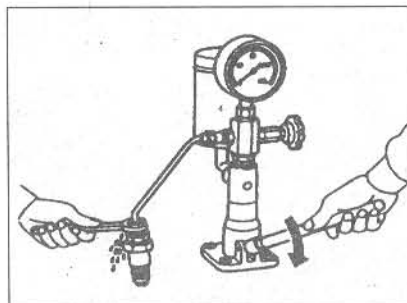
Проверка давления начала впрыска (Глава 37)
